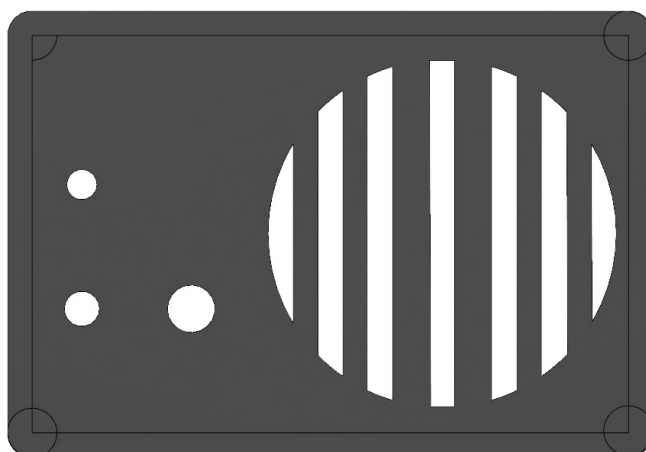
Печать крышки корпуса радиоприёмника на 3D принтере
